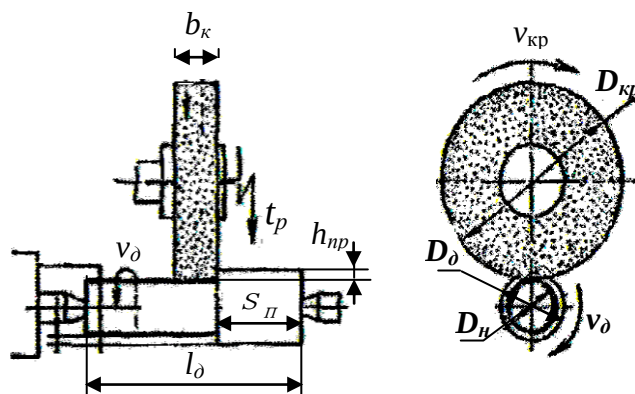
Схема обробки шліфувальним кругом деталей класу "вали":
